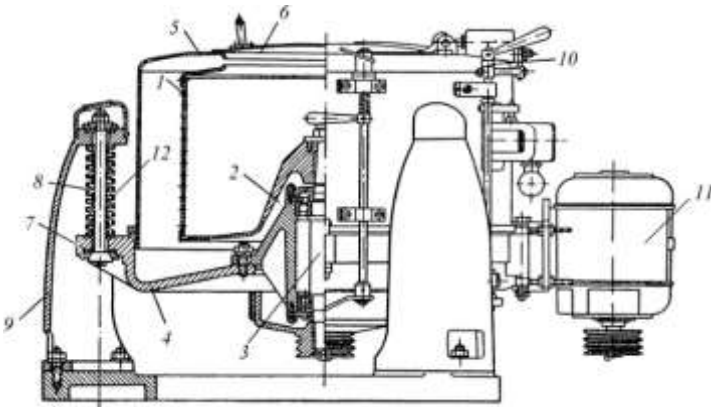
Триколонна центрифуга: 1 – ротор; 2 – конус; 3 – вал; 4 – днище; 5 – кожух; 6 – кришка; 7 – станина; 8 – тяга; 9 – колонка; 10 – гальмо; 11 – двигун; 12 – пружина
